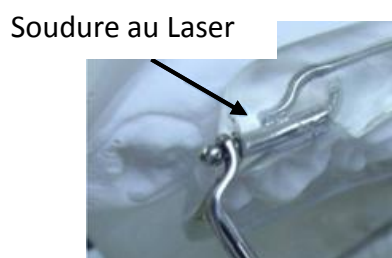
Soudure au Laser (PUL CONCEPT)
